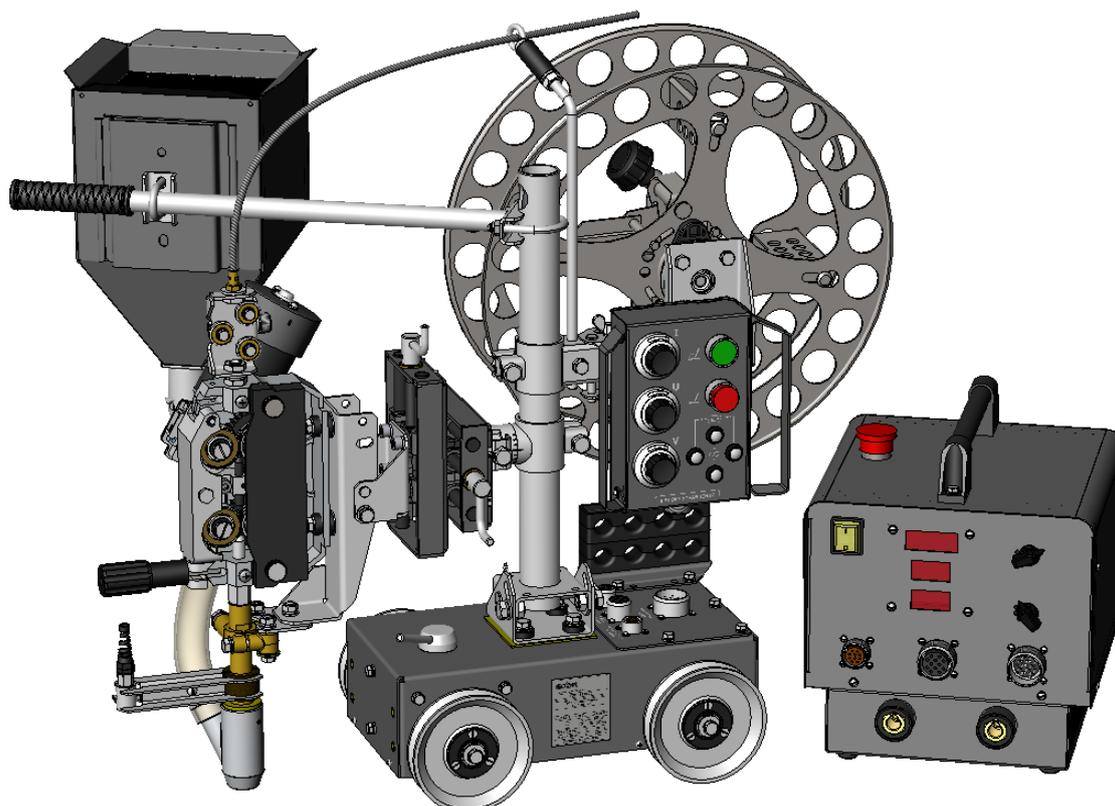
Автомат сварочный АДГ-630 исп.-02
